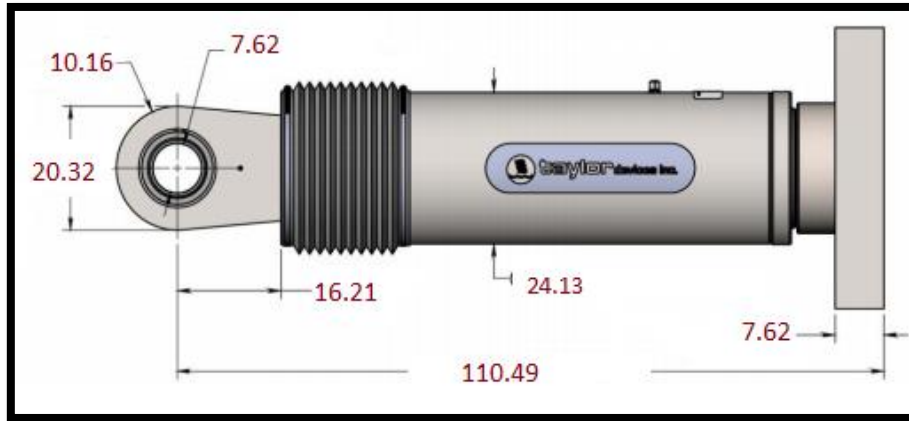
Dimensiones del disipador de 330 kip. Fuente: Propia
